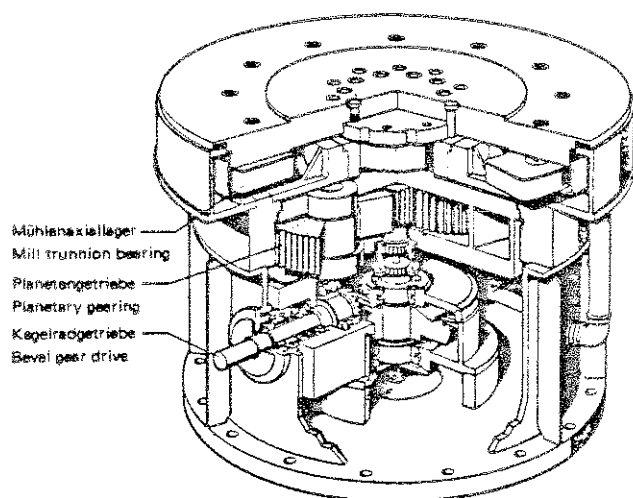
b. Walzenmühlenantrieb mit Mühlentrunkionlager, Planetengetriebe und Kegelradgetriebe
